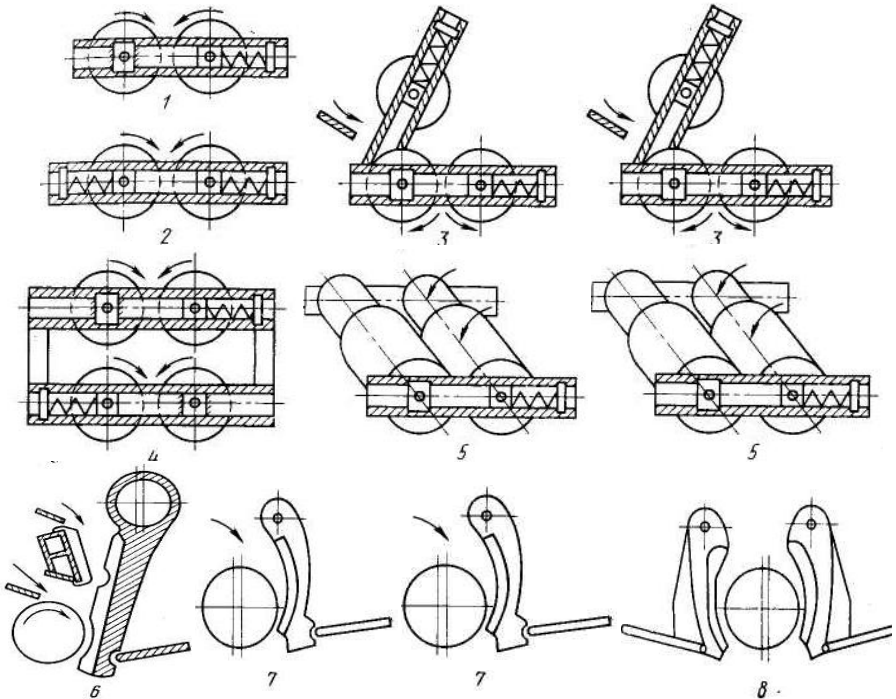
Конструкційні схеми валкових дробарок
